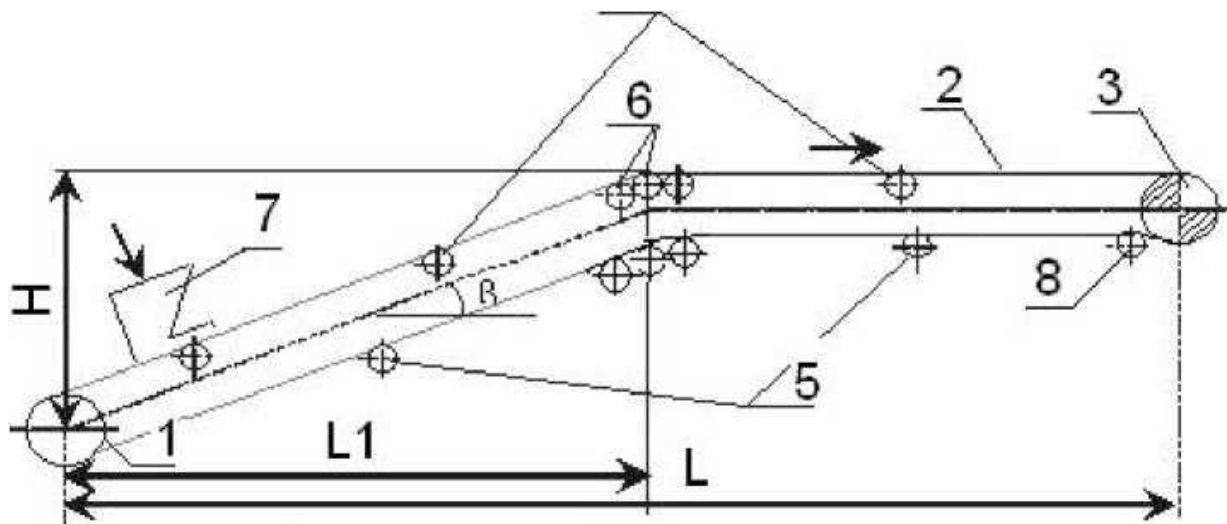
Схема принципова стрічкового конвеєра
